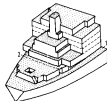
Схематический чертеж кормовой надстройки на теплоходе „Пестово“ (тип „Варшавяк“) 1 — верхняя палуба; 2 — подпалубное пространство
